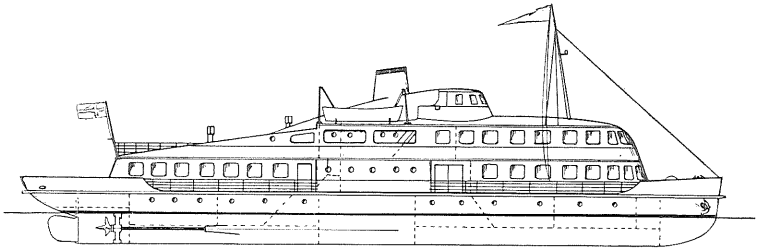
Mindre passagermotorskib med negativt spring i overbygningerne.
